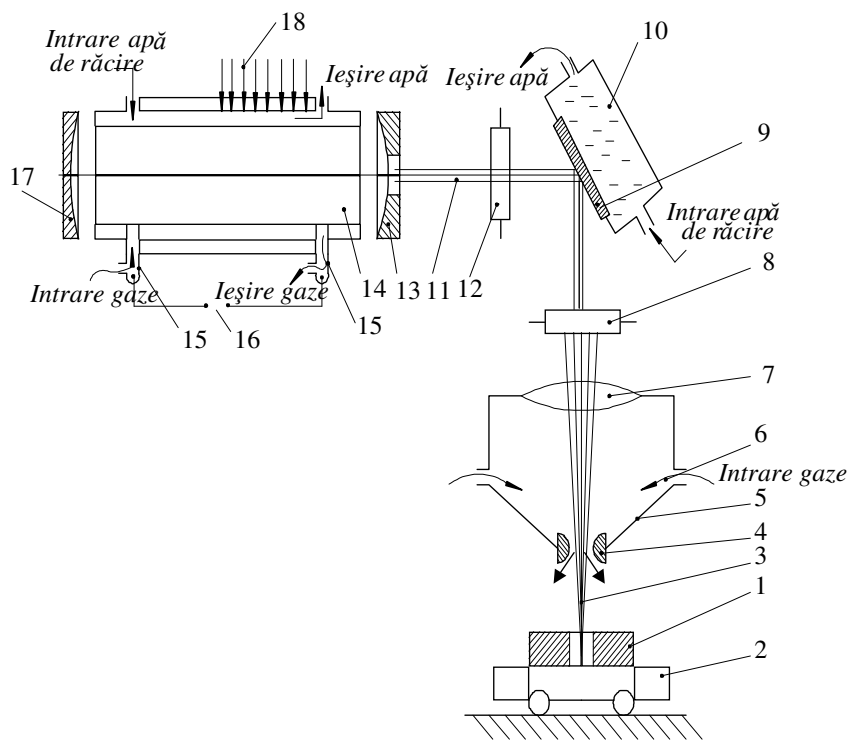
Schema de principiu a unei instalații de prelucrare dimensională cu fascicul laser, cu mediu activ gazos:
